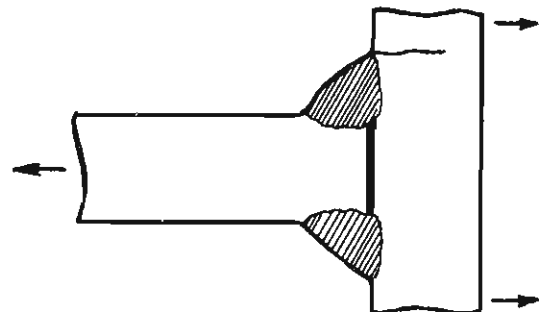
Fissuration par fatigue d'une soudure en T lorsque l'élément transversal subit un effort de flexion.
